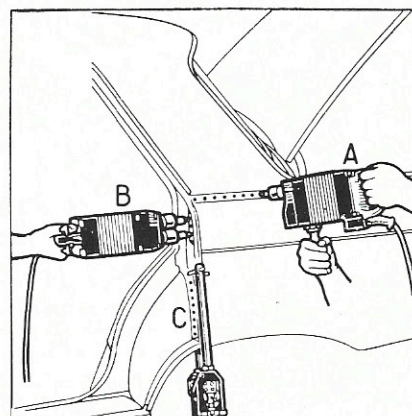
A. Soudage du panneau d'aile arrière gauche sur panneau de custode (double point DP 38). - B et C. Soudage du panneau d'aile sur passage de roue (B ; double point DP 38 partie supérieure - C ; porte-électrodes 244 A partie inférieure). Soudeuse et pince ARO.
